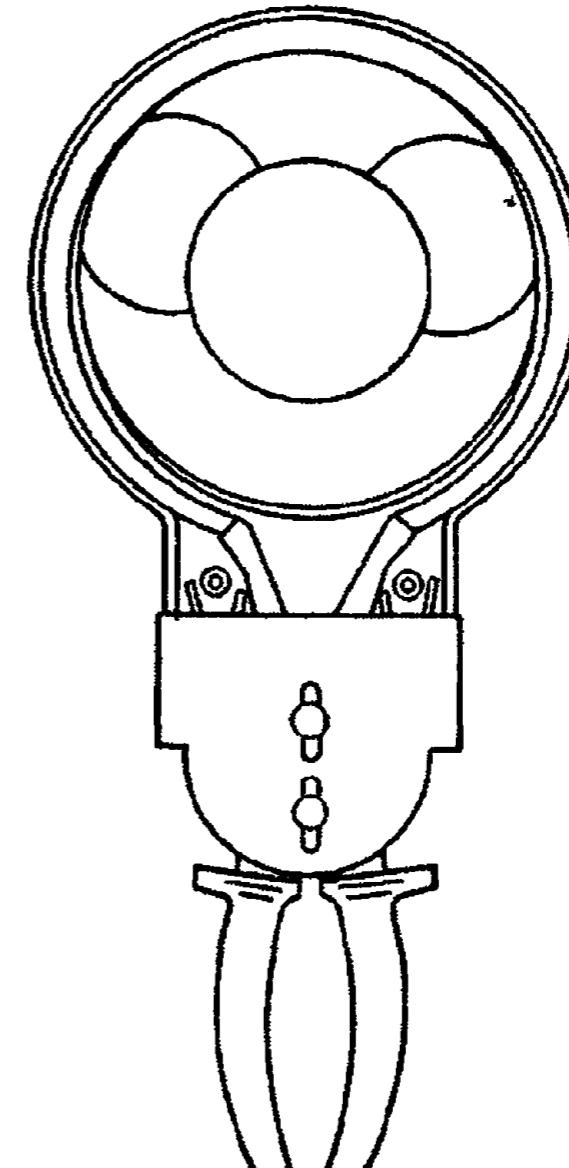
Приспособление И801.08.000 для снятия и установки поршневых колец
